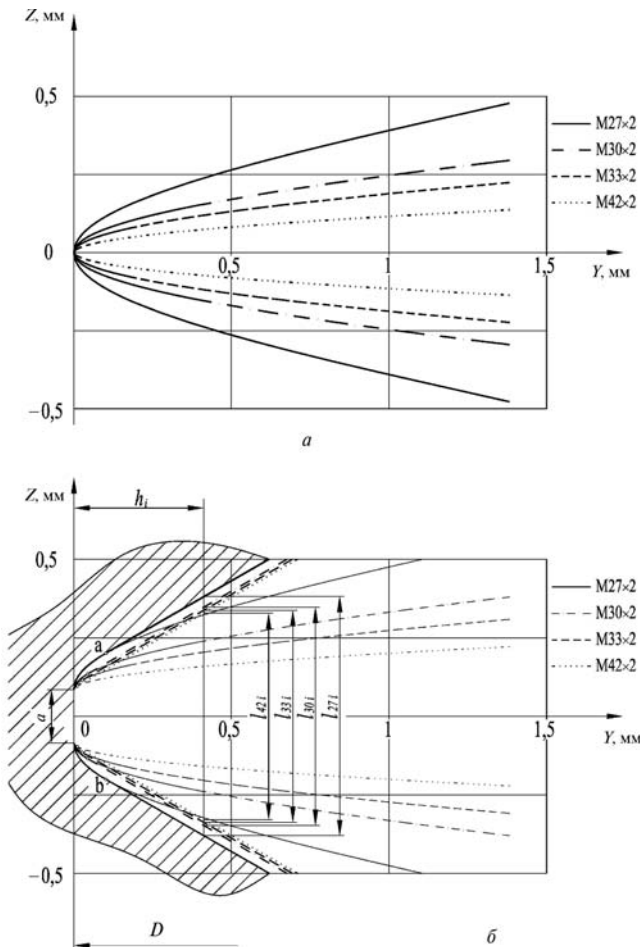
Расчетные траектории движения вершины зуба резцообразующей части сверло-резцовой фрезы (а) и расчетные профили впадины формируемой резьбы (б)
